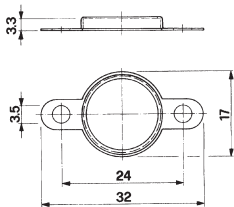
Flansch mit beidseitiger Befestigung, gekröpft
